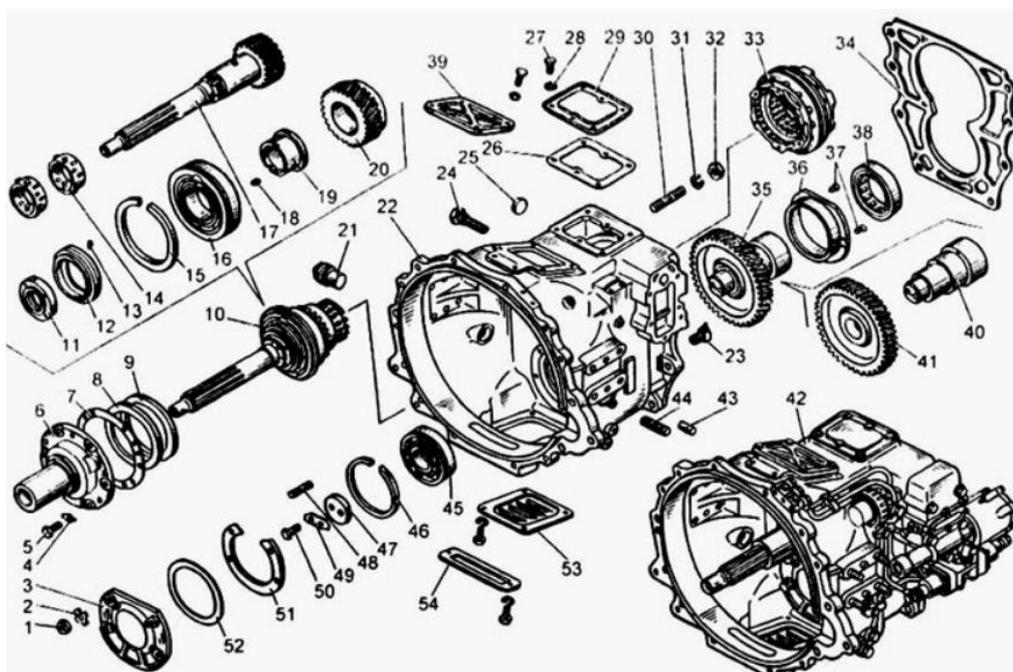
Устройство коробки передач КАМАЗ –65115
